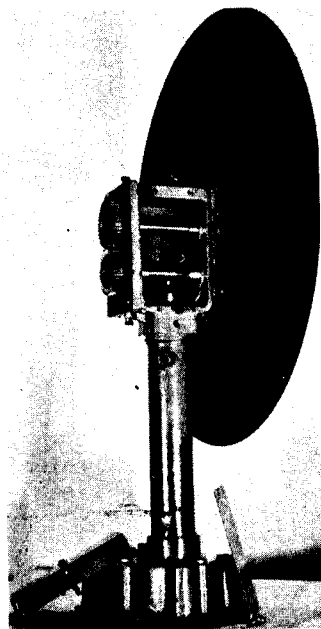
Vista posterior del indicador de posición con la tapa del engranaje removida.
